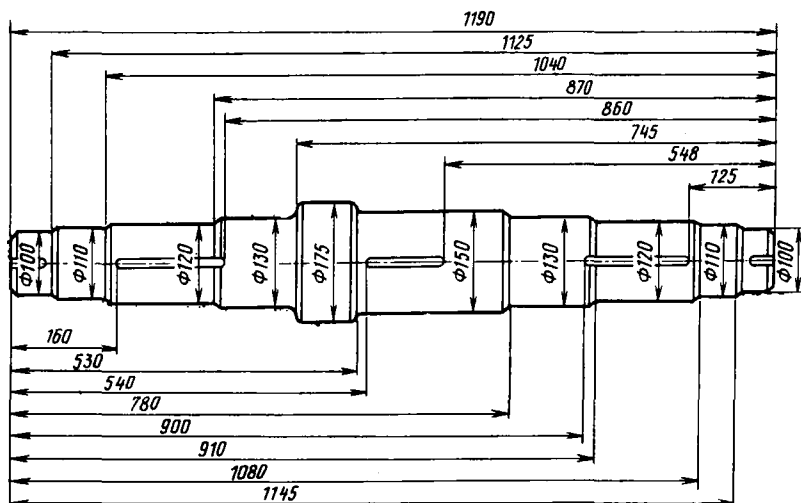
Главный приводной вал эскалатора ЛП-7К
